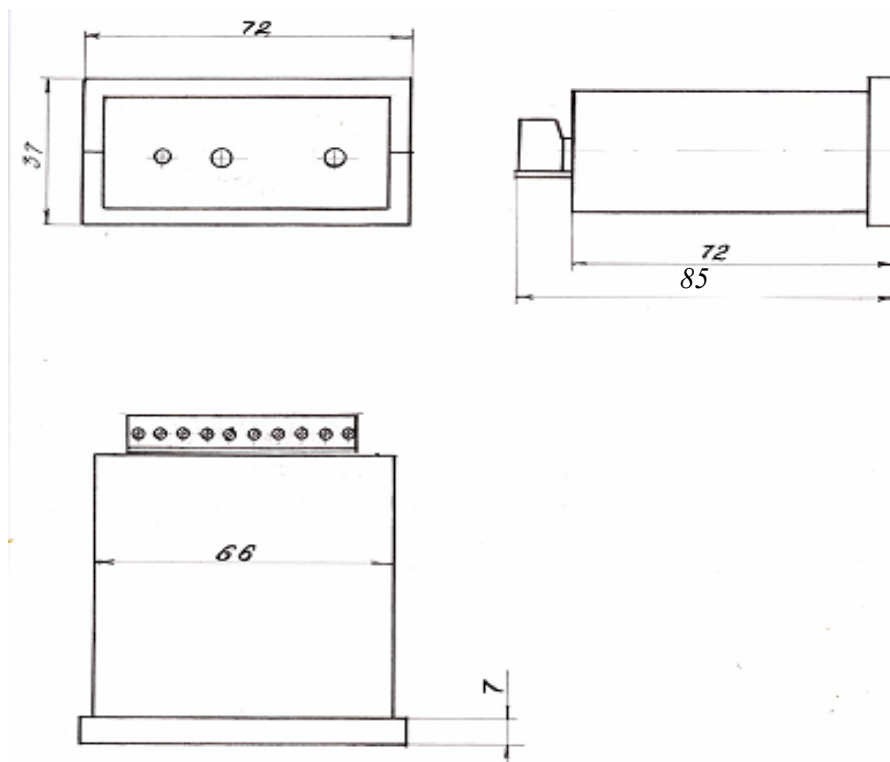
Габаритные, установочные и присоединительные размеры реле
